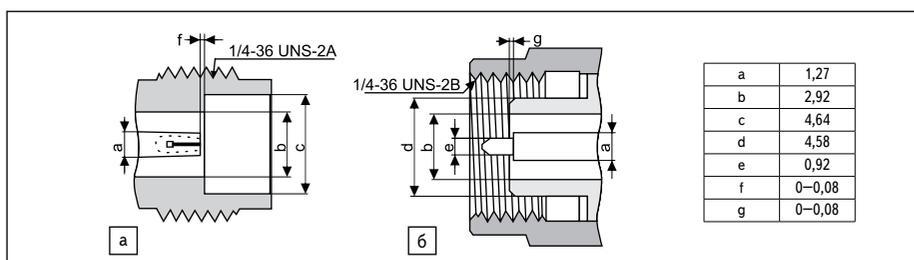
Интерфейс 2,9-мм соединителя: а) розетка; б) вилка
